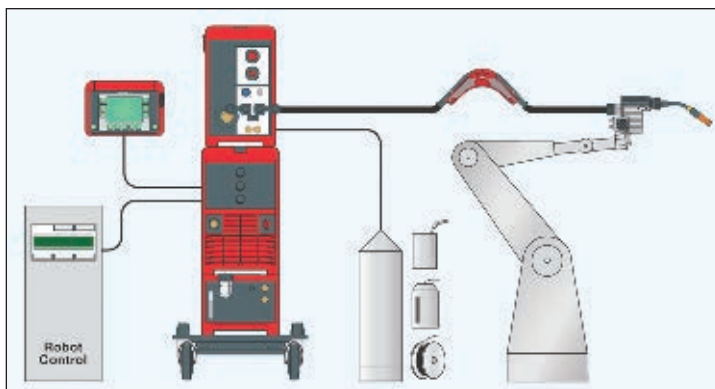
Схема сварочного комплекса с использованием робота при СМТ-процессе
